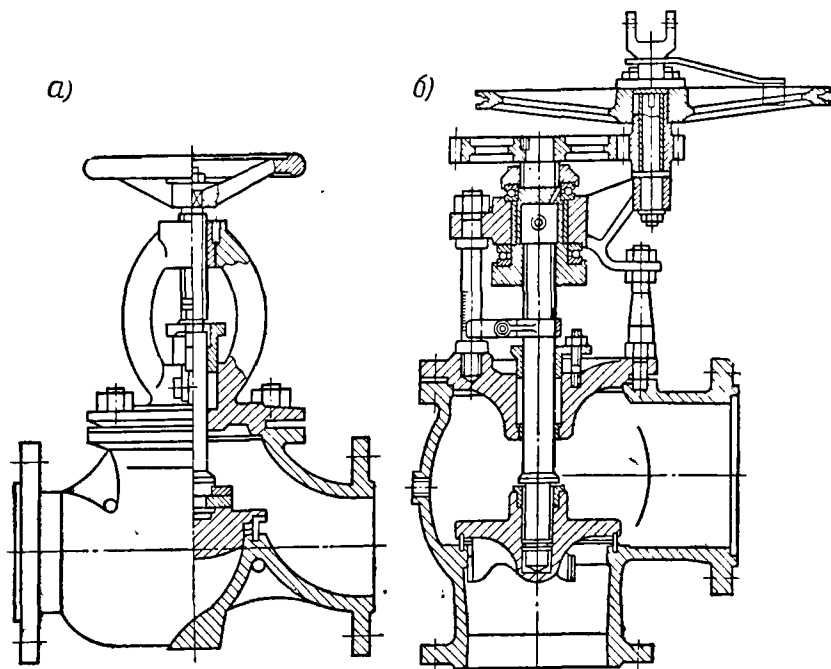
Прямой разобшительный (а) и угловой стопорный (б) клапаны
